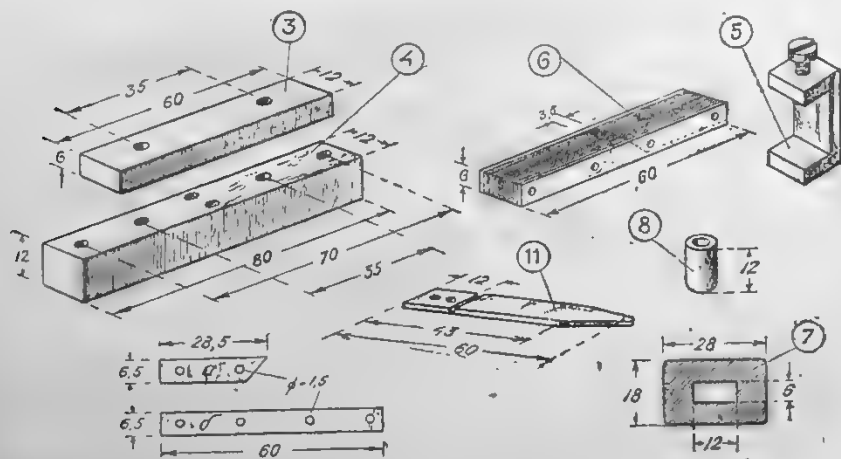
и 4 — бруски для укрепления магнита, 5 — скобка для закрепления сердечника, 6 — сердечник, а — железная пластинка, б — латунная или медная обойма, 7 — щетки-катушки, 8 — трубка стойка, 11 — вибратор.
